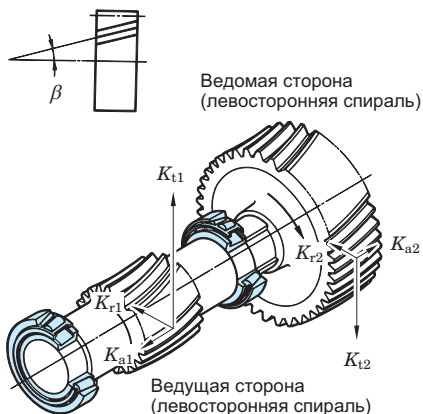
Нагрузки на цилиндрические косозубые передачи
